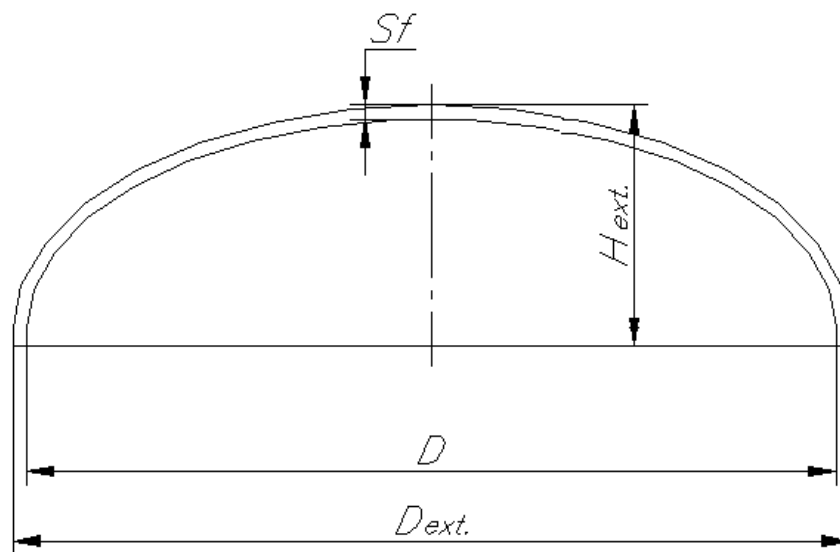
Dimensiones del cuerpo de la manta de calentamiento.
